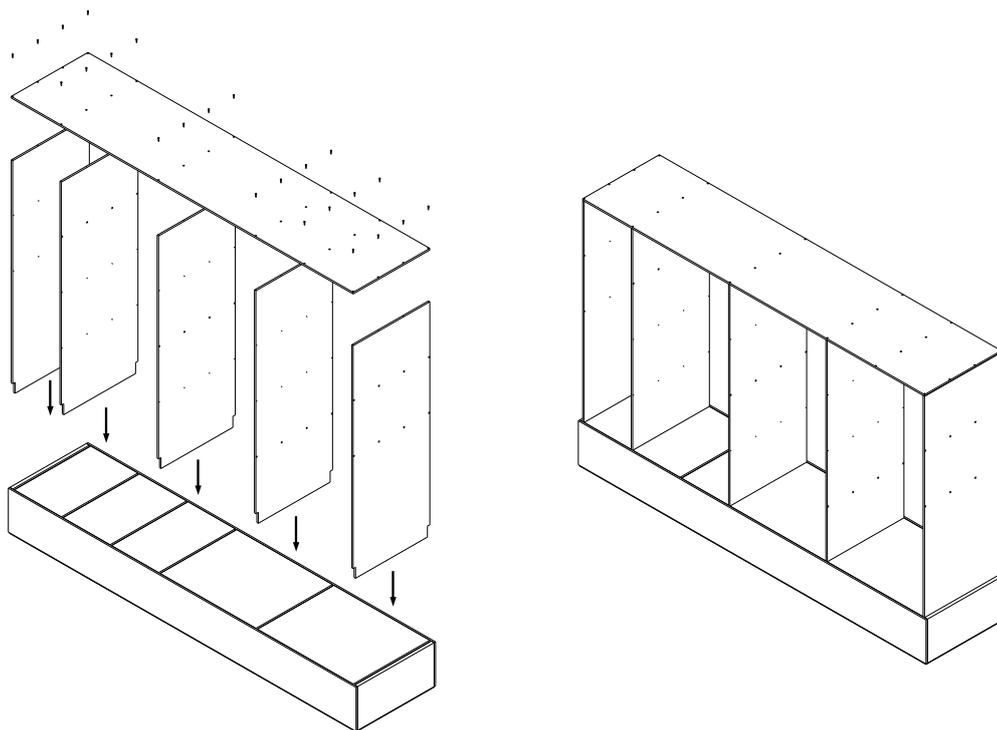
Despiece y montaje planchas 1, 2, 3, 4 y 5 sobre pedestal
